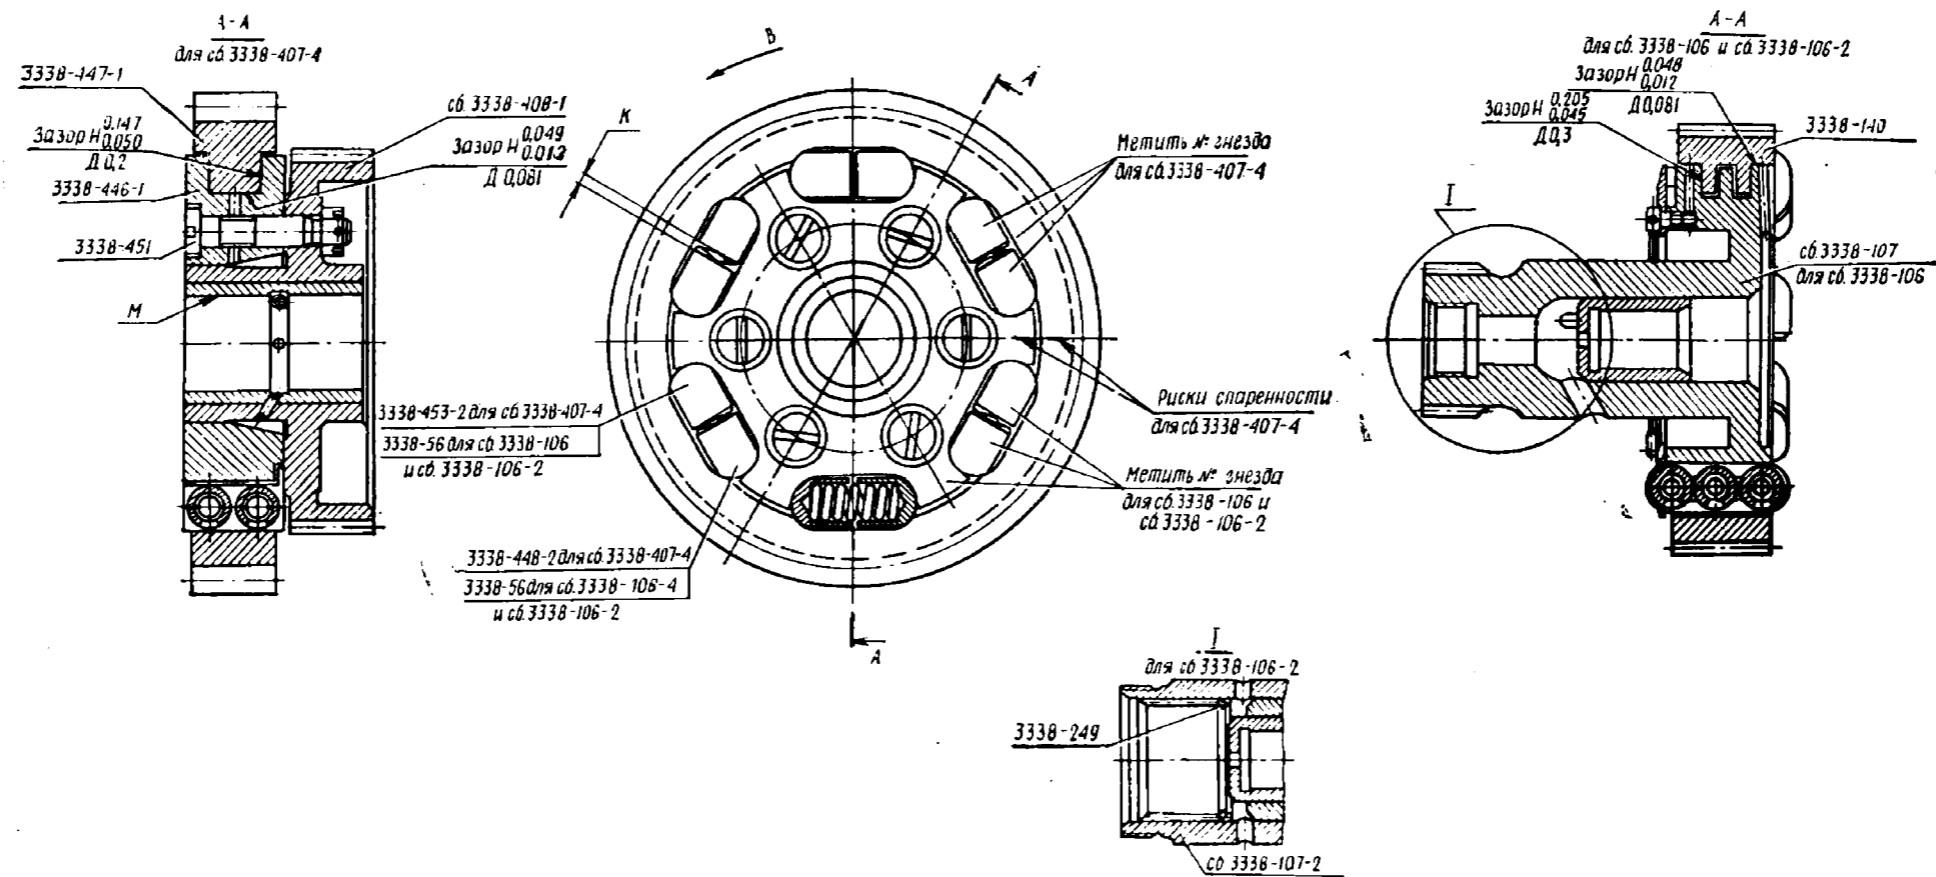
Ведущая шестерня сб.3338-106, сб.3338-106-2 и блок шестерен сб.3338-407-4:
